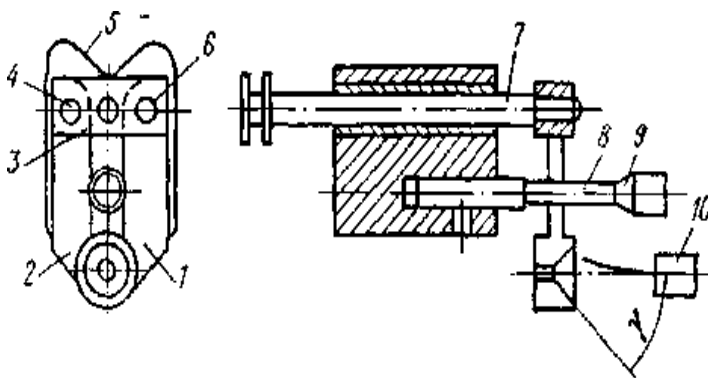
Корректор для сборки изделий с гибкими выводами.
